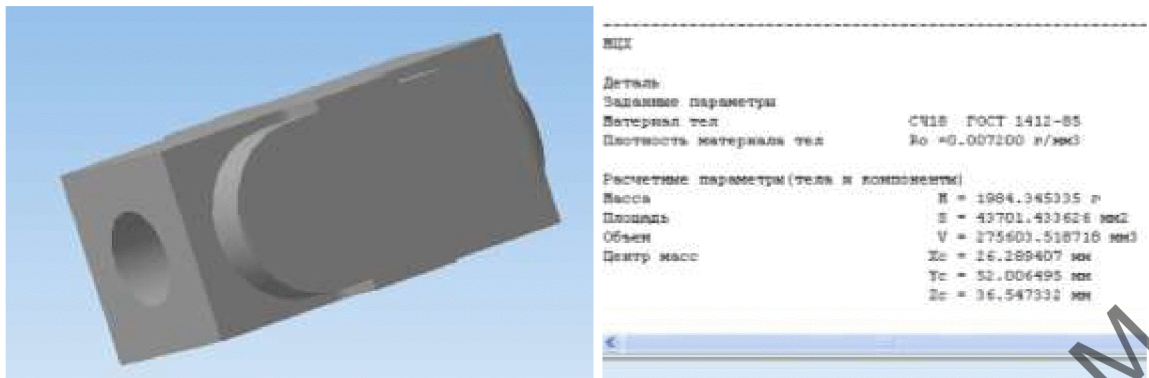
Визначення маси заготовки для лиття за виплавними моделями
